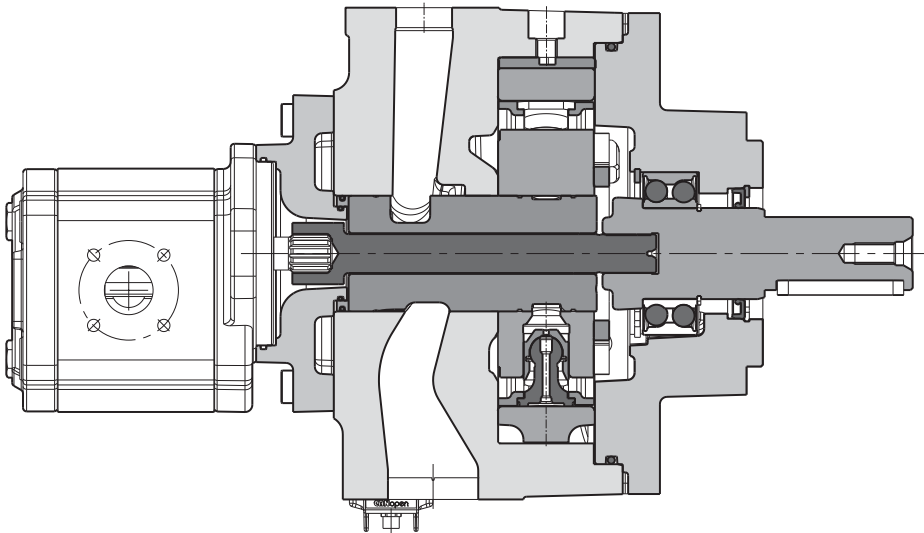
Radialkolbenpumpe mit angebaute Zahnradpumpe mit SAE-B-Adapter
